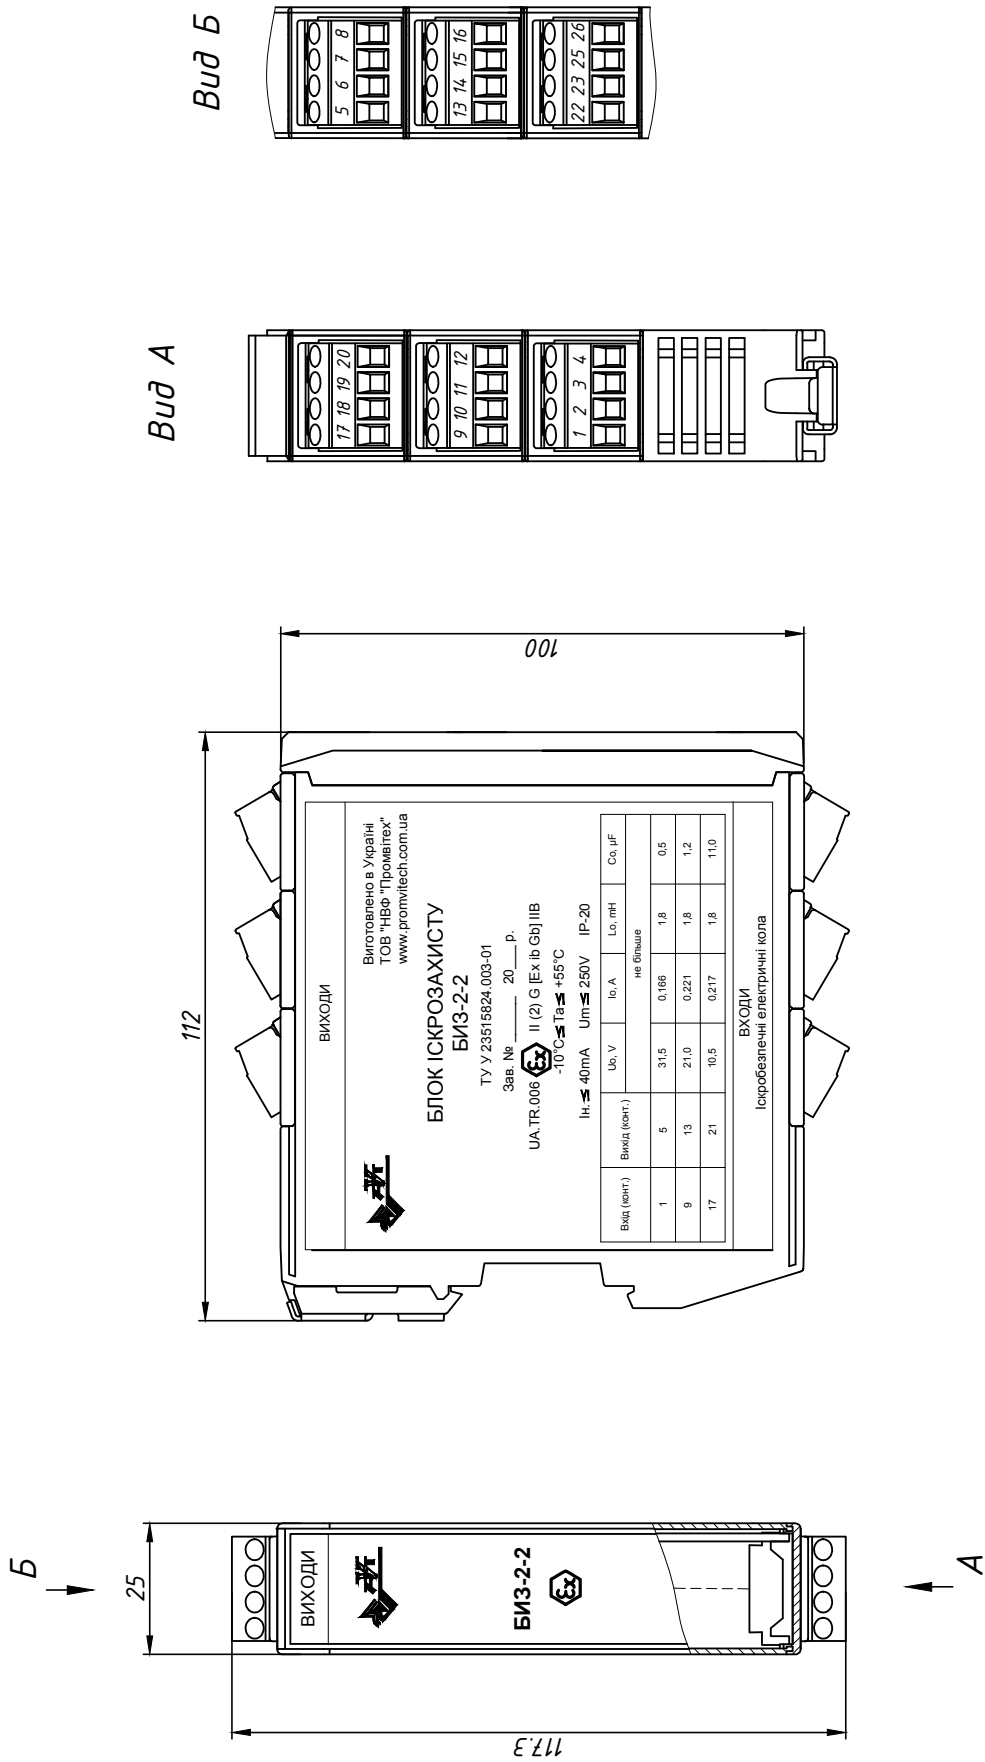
Блок искрозащиты БИЗ-2-2, габаритные, присоединительные и установочные размеры
